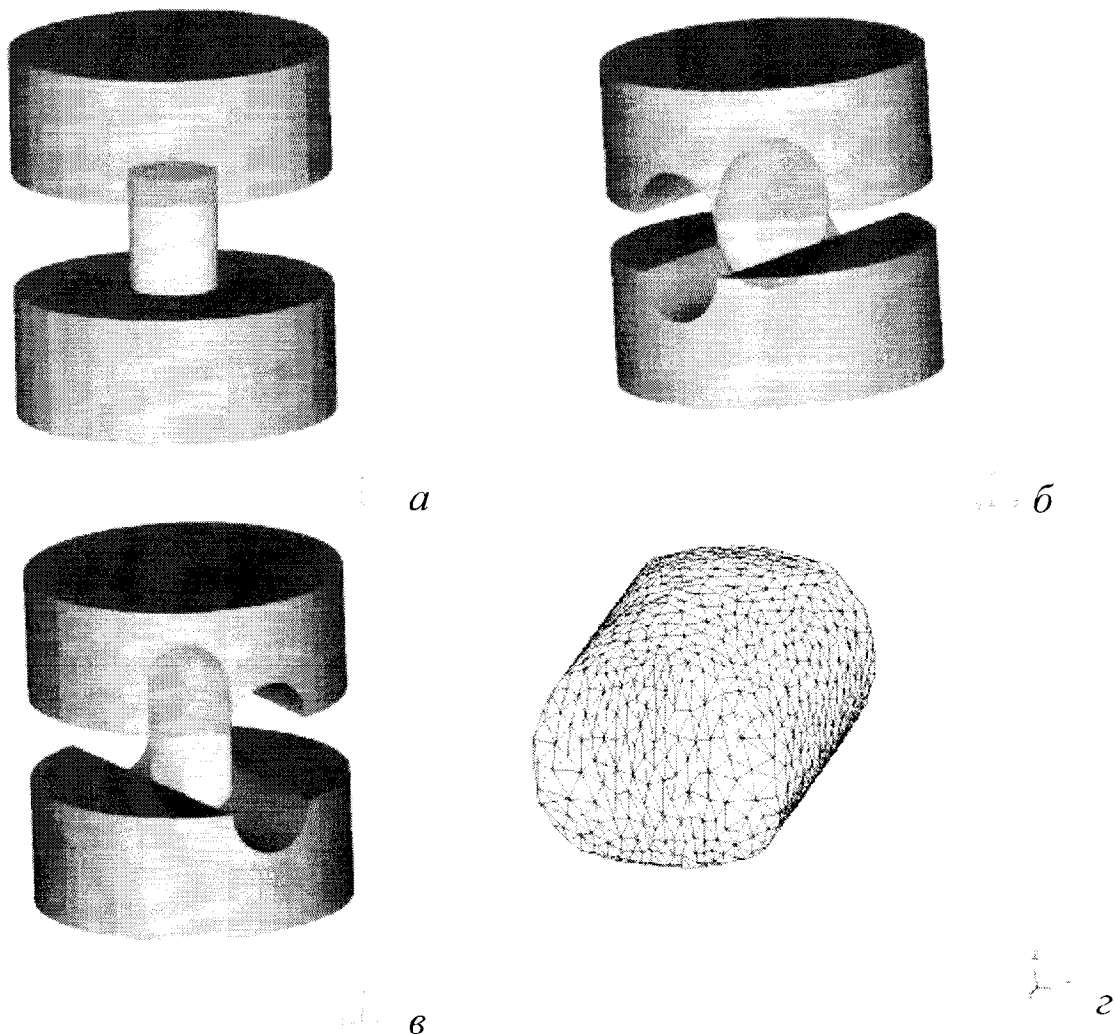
Последовательность операций всестороннейковки цилиндрической заготовки:
